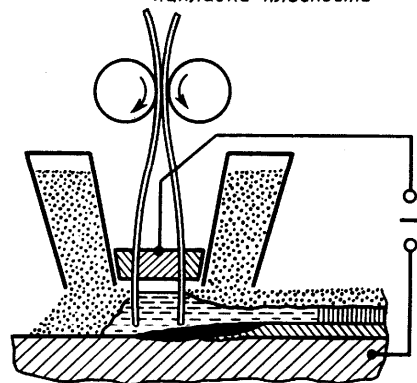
Схема электрошлаковой наплавки двумя лентами
